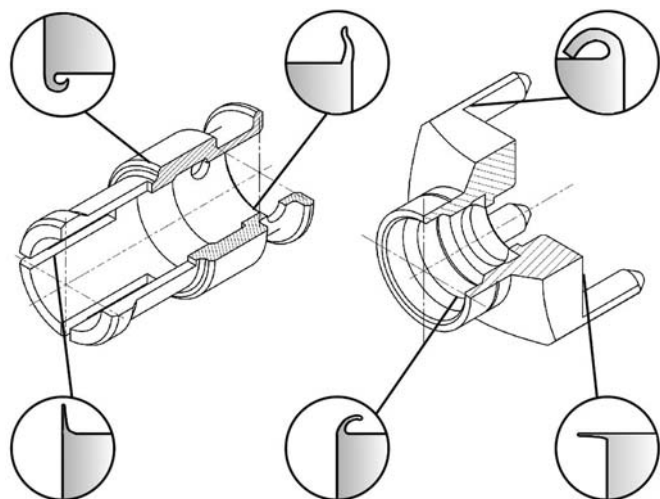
Расположение и форма заусенцев на заготовках деталей РЭА
